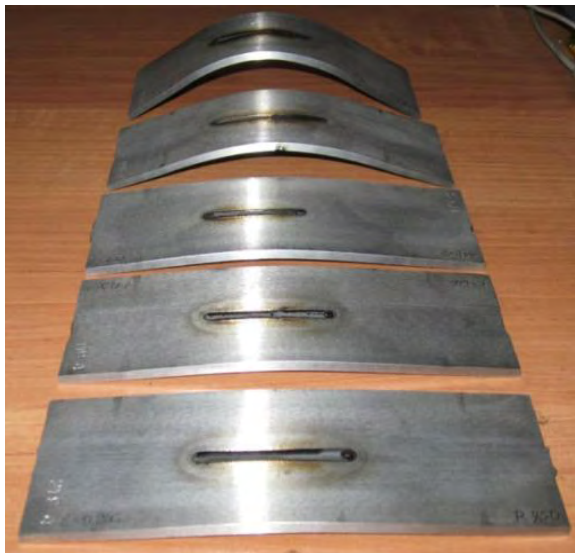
Общий вид образцов после сварки на установке Varestraint-test с принудительным деформированием на оправках различного радиуса
